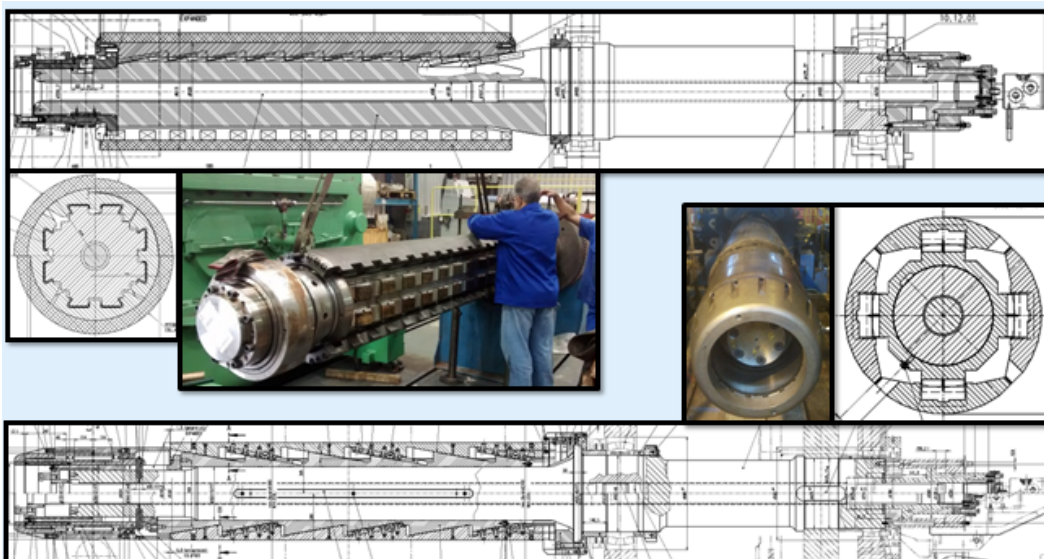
Desenho de conjunto geral e foto de mandris de laminadores de encruamento / acabamento.
